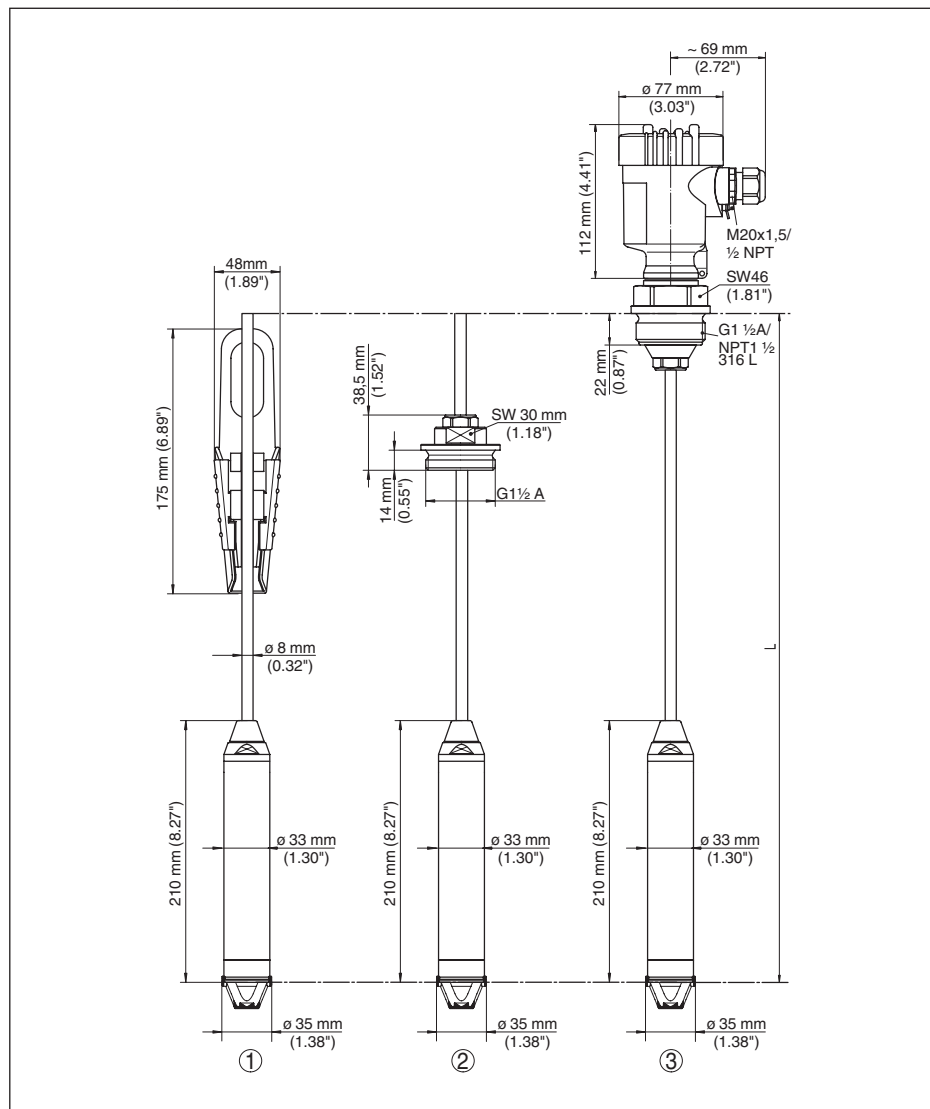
VEGAWELL 52, com sensor de titânio 33 mm
